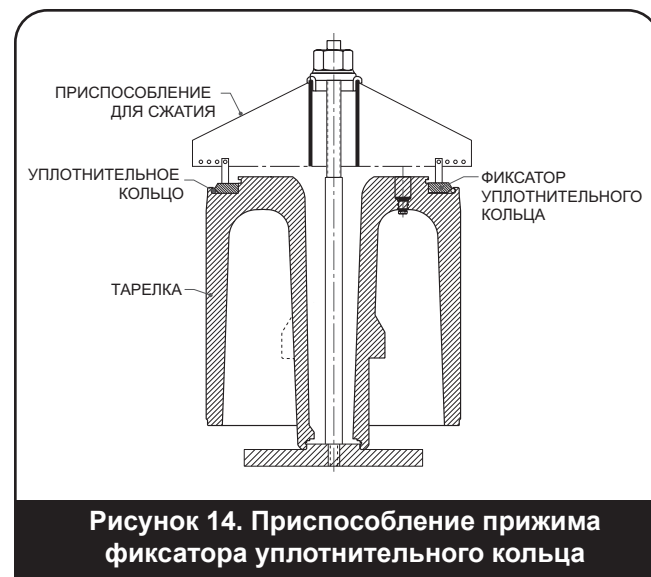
Приспособление прижима фиксатора уплотнительного кольца
